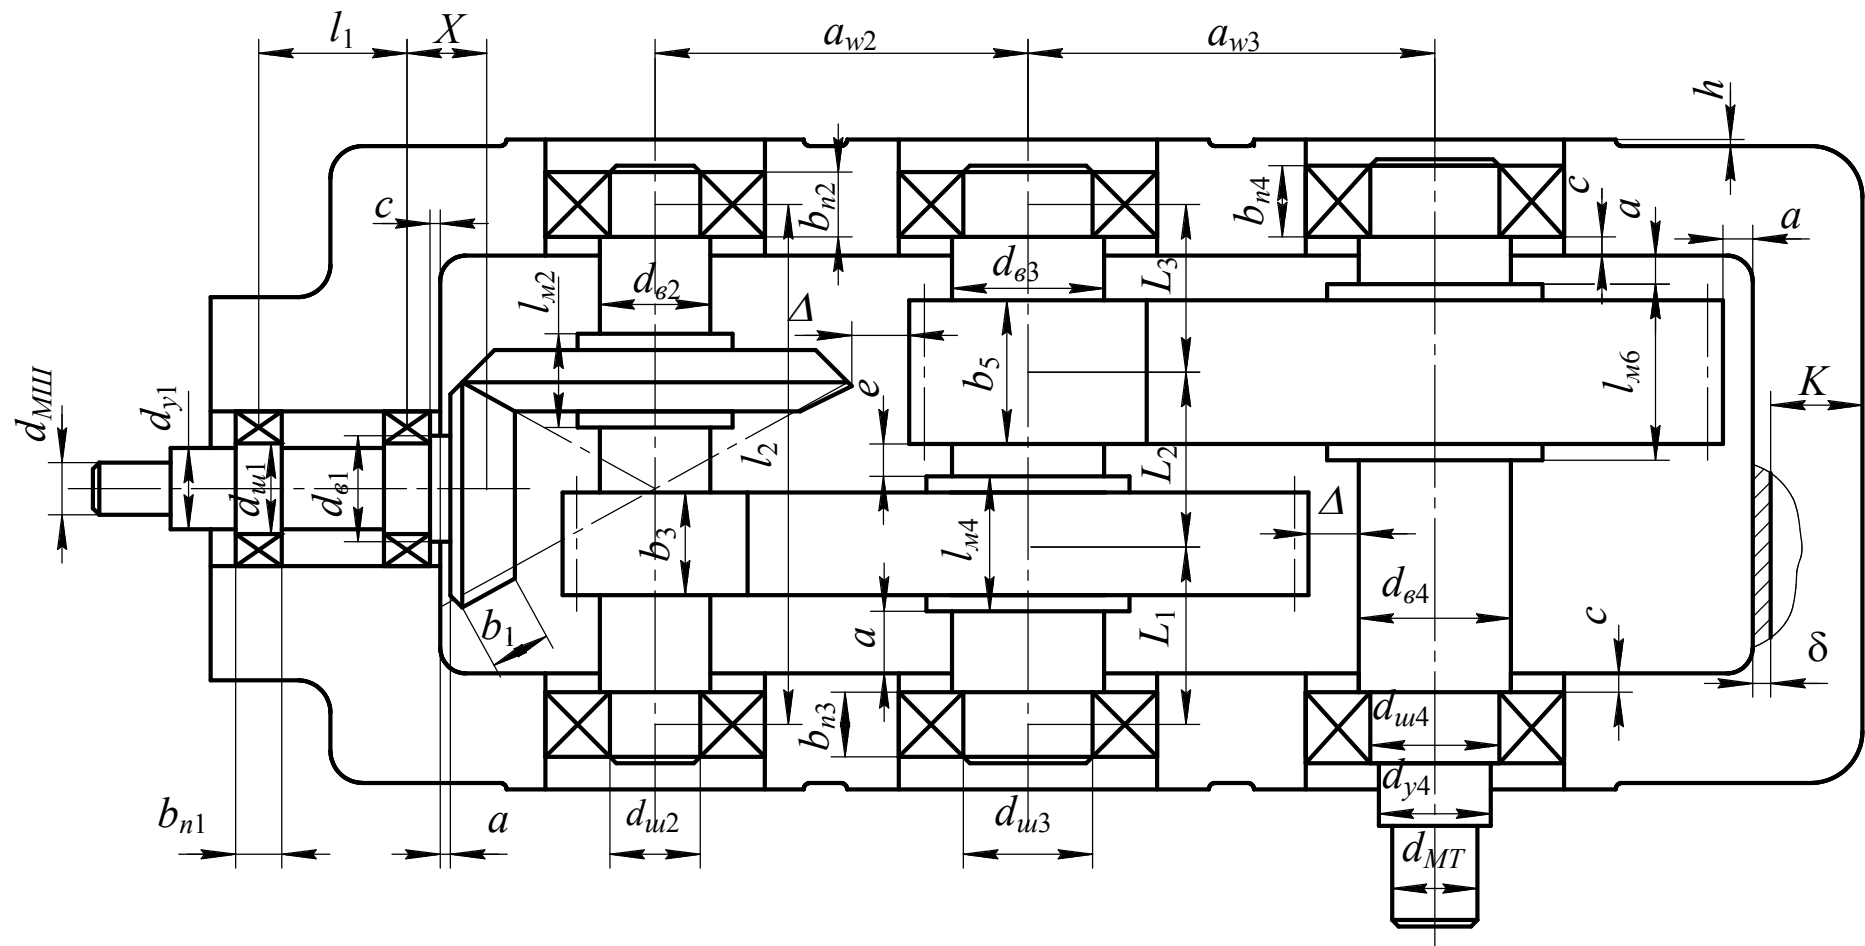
Эскизная компоновка трехступенчатого коническо-цилиндрического редуктора
